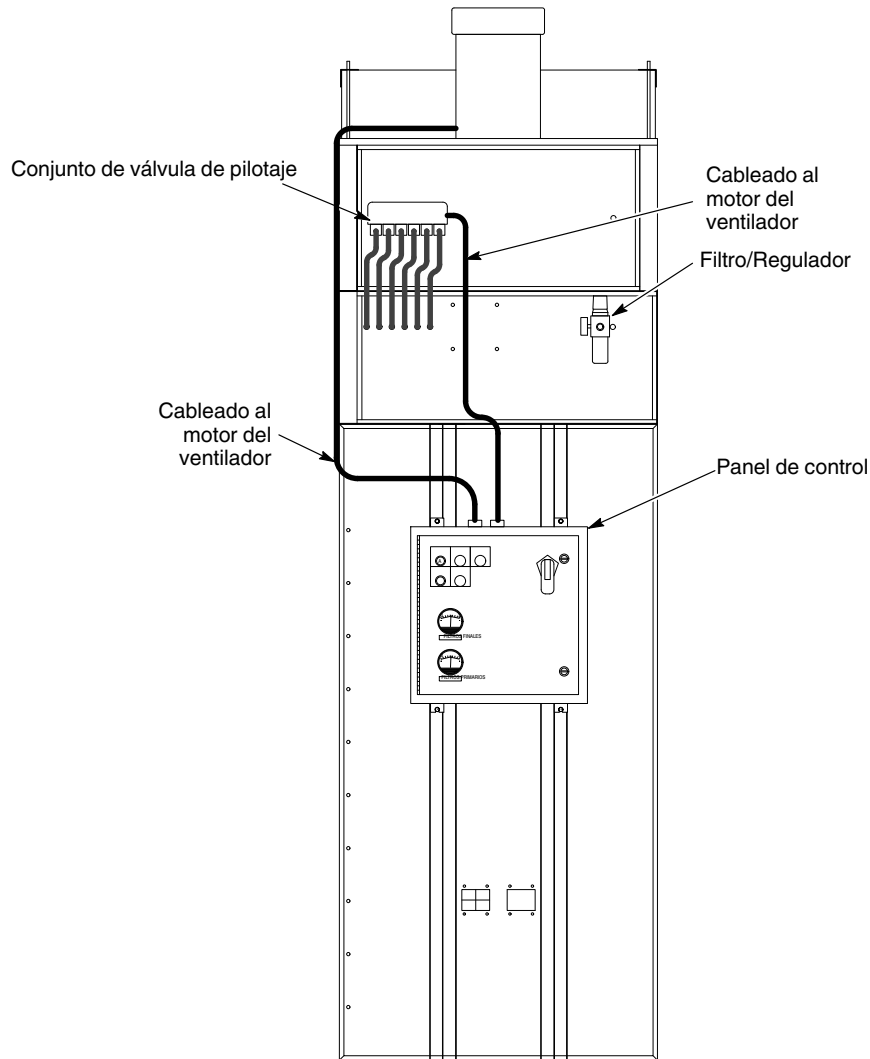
Instalación del panel de control, del conjunto de válvula de pilotaje y del filtro/regulador (se muestra orientación izquierda)
